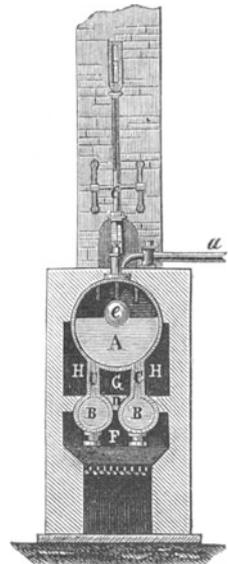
Dampfkesselanlage für Hochdruckmaschinen.
